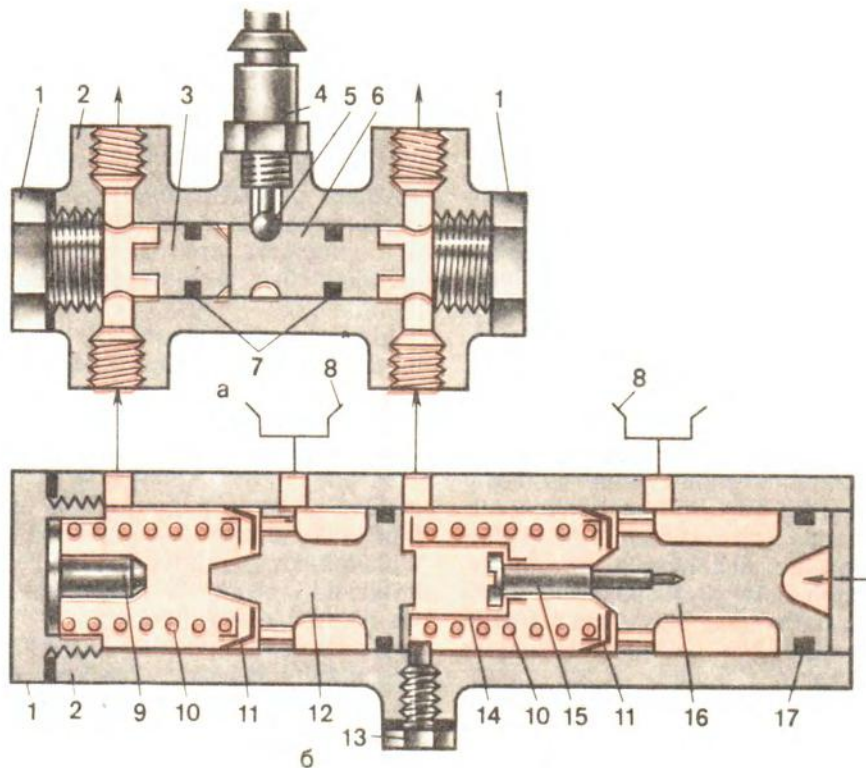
Схема аварийного сигнализатора (а) и главного тормозного цилиндра (б) автомобиля УАЗ-3303:
